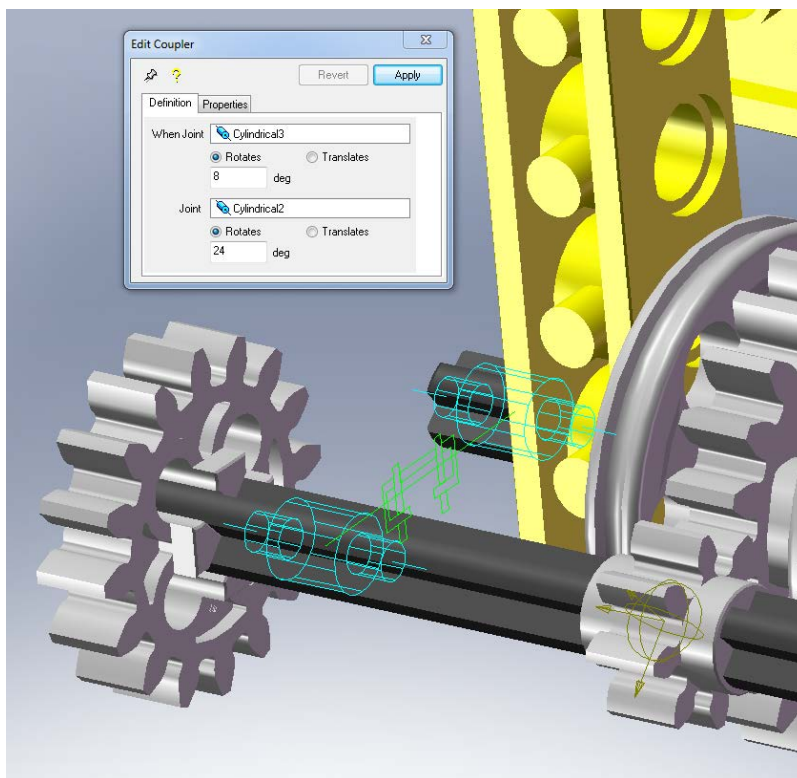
Acoplamiento entre engranajes de 8 y 24 dientes.
